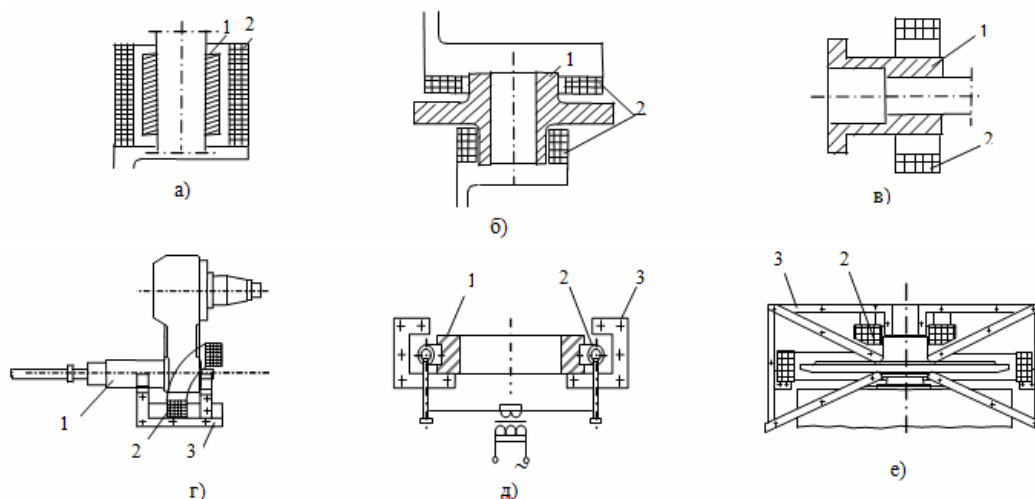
Схемы типовых индукторов, охватывающих деталь:
